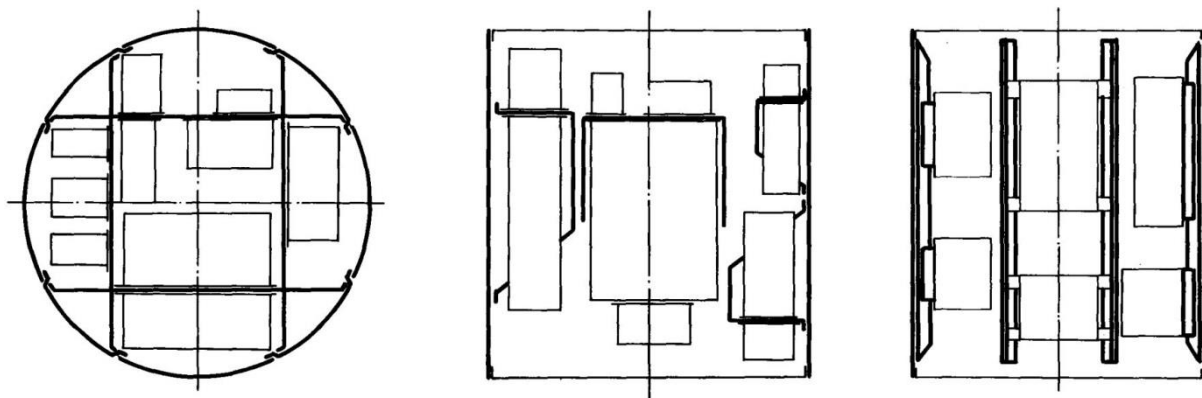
а) - кріплення приладів на рамі; б) - на кронштейнах; в) - на силовому наборі
